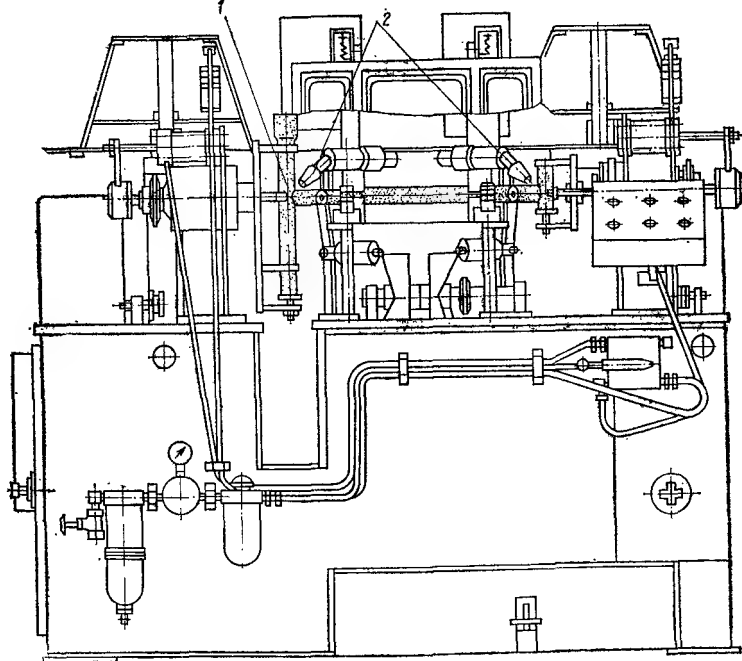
Полуавтомат для сварки Т-образных соединений СТД-131
